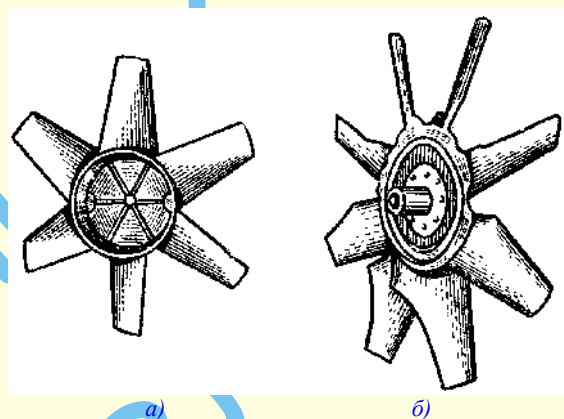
Осевое лопаточное рабочее колесо: а — сварное; б — штампованное
